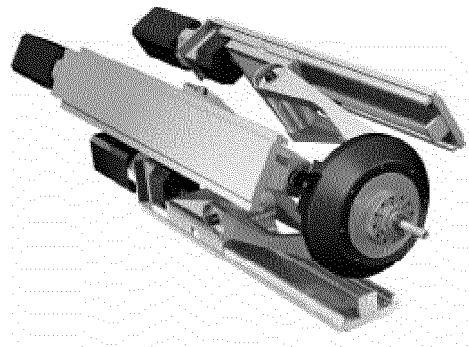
Фрезерна головка SPRINT Z3 «DS TECHNOLOGIE» (Німеччина)
